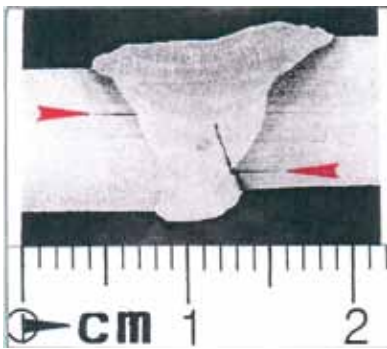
Querschliff einer fallnahtgeschweißten Stumpfnahnt mit Längsris und Doppelungen im Grundwerkstoff
